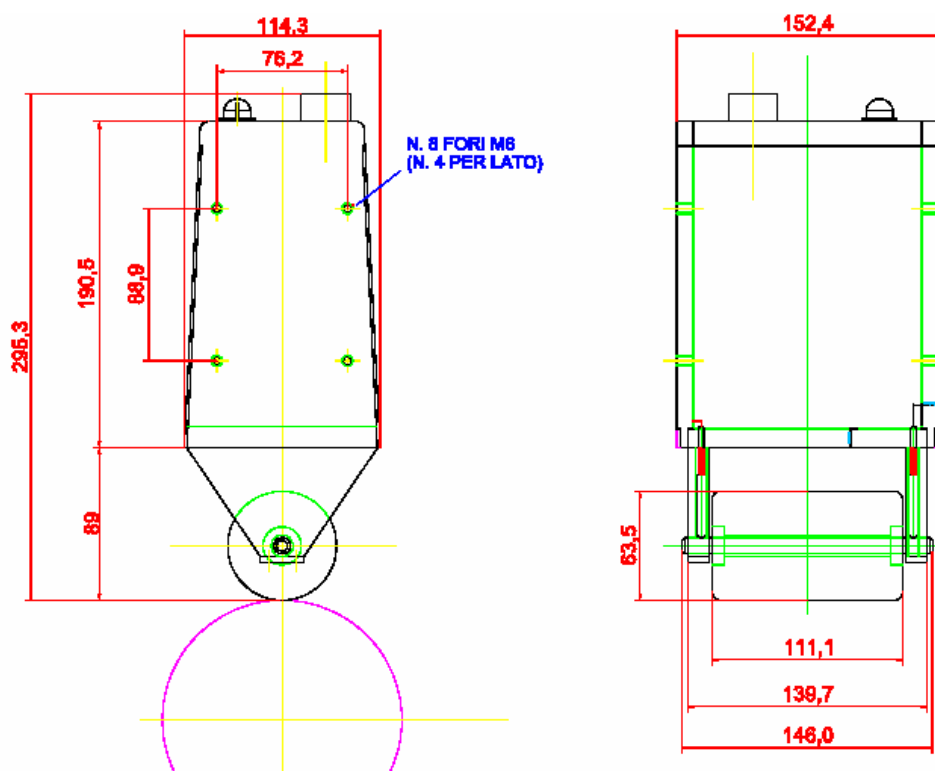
Dimensioni di ingombro e installazione Rilevatore Giunte mod. 1032C
